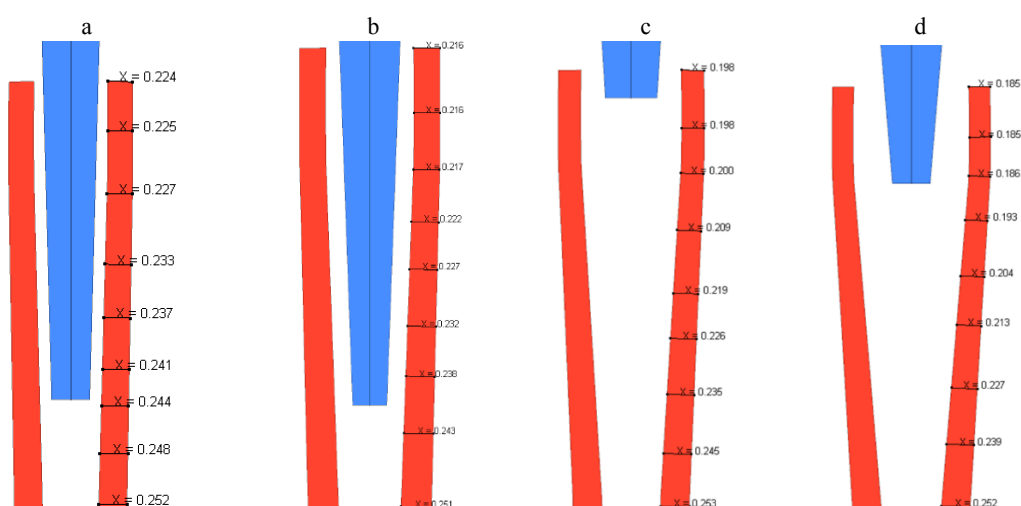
Изменение размеров заготовки в процессе раздачи для переходов: а – 1; б – 2; с – 3; д – 4
